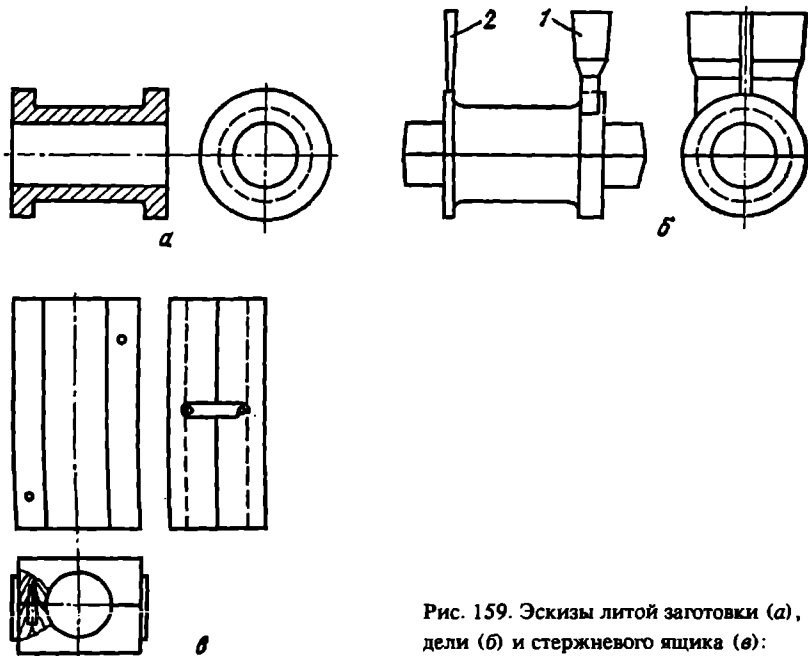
Эскизы литой заготовки (а), модели (б) и стержневого ящика (в):
